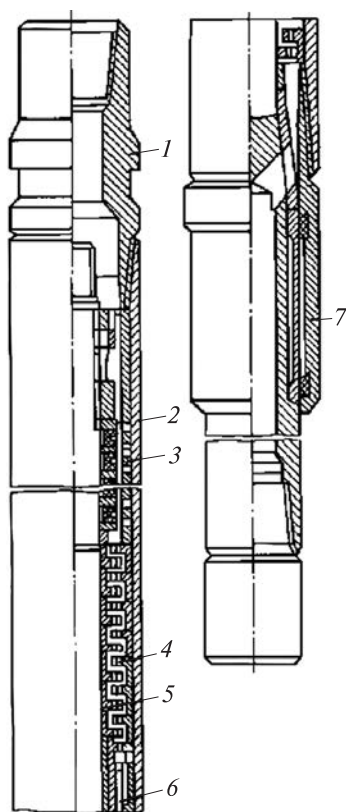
Схема односекційного багатоступінчастого турбобура: 1 — перевідник; 2 — трубчастий корпус; 3 — осьова опора; 4 — комплект ступенів турбіни; 5 — вал турбобура; 6 — проміжні гумово-металеві радіальні опори; 7 — ніпель
